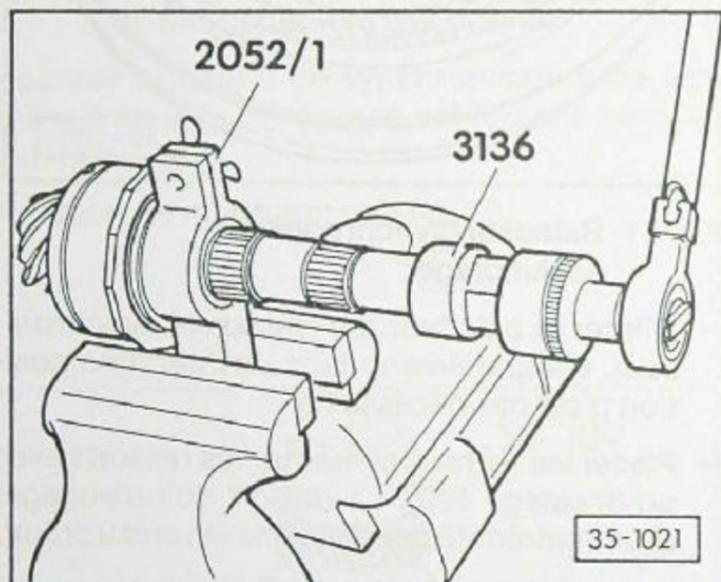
Bague intérieure/roulement à aiguilles: desserrage et serrage
